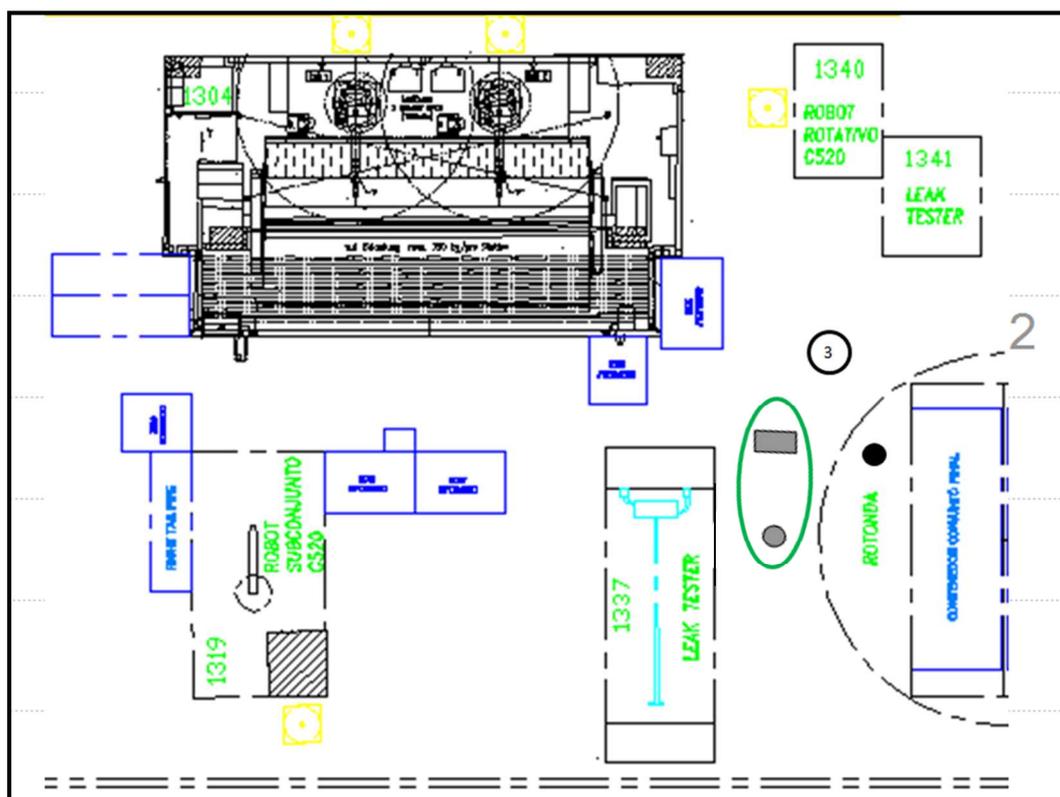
Nuevo layout línea C520. Recuperado de: 'Nuevo layout C520 v1' (2017)
